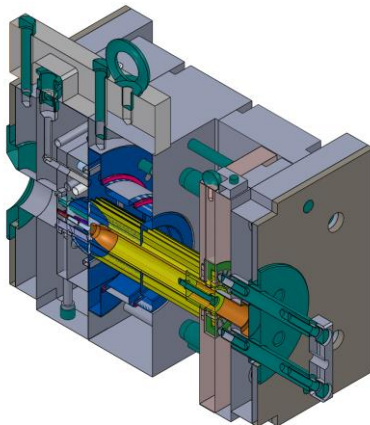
Schnittbild des Spritzgießwerkzeugs mit Formein-
